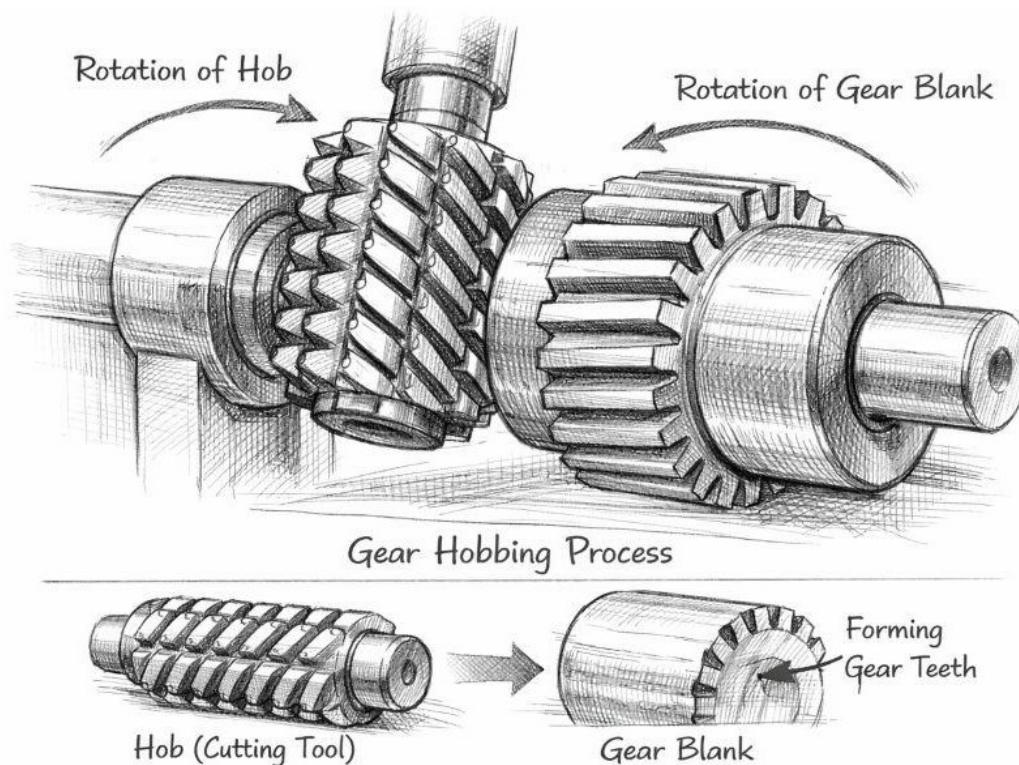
Формоутворюючі рухи при черв'ячному зубофрезеруванні.
